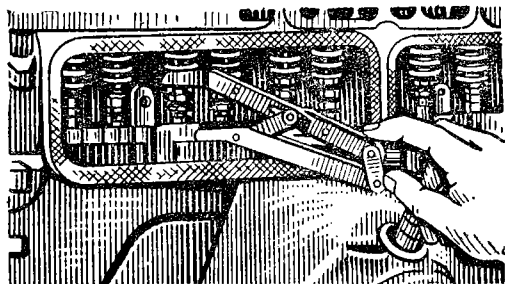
Сжатие пружины клапана специальным приспособлением для снятия клапанных пружин
